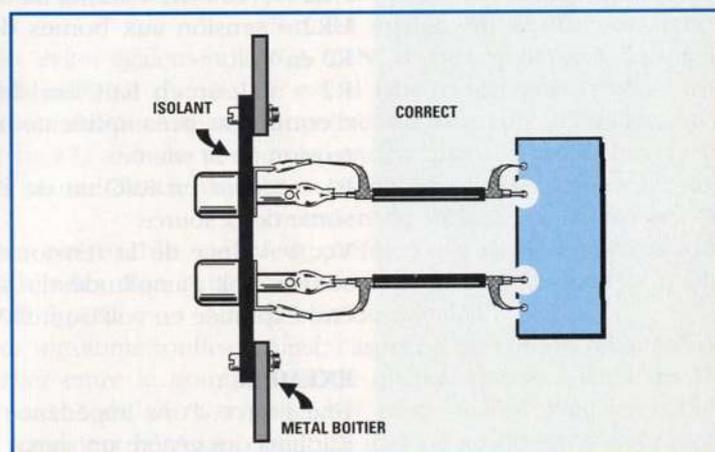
Après avoir fixé ce support plastique sur le boîtier métallique, relier la tresse blindée sur la masse de la prise BF (voir fig.13) de façon à la tenir isolée du boîtier.
